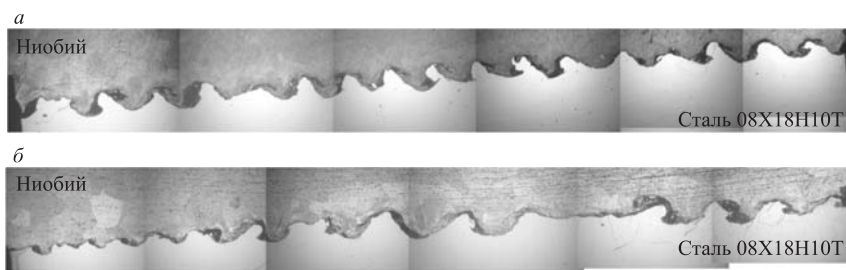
Макроструктура сварного соединения ниобий+сталь 08X18H10T: а) образец №1; б) образец №2
